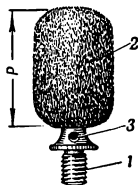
Пуховка-помазок для смазывания канала ствола после чистки:
